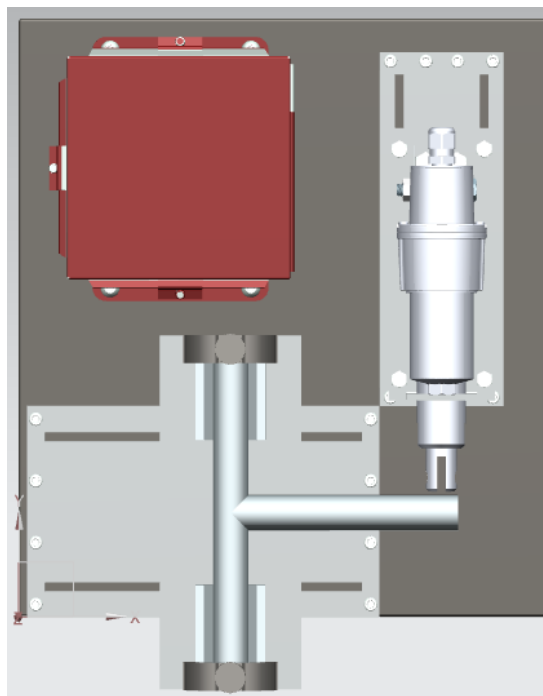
Vista superior de máquina con probeta a 90° montada.
